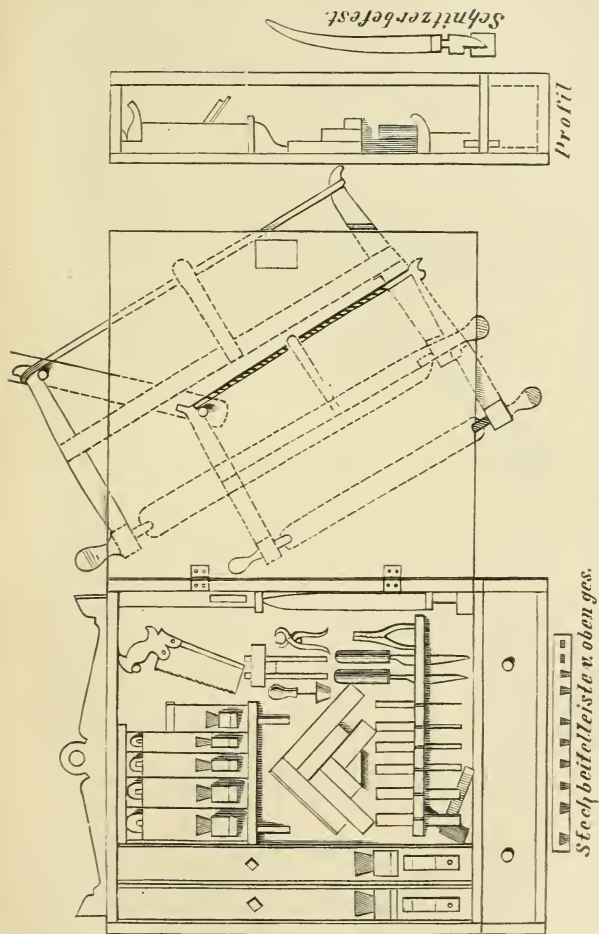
Werkzeugschrank in der Hobelbankwerkstatt.
